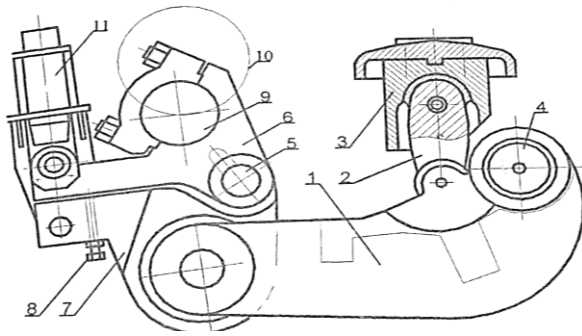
Конструкція механізму пресування коліно-важільного преса с розрізним шатуном: 1 – важіль пресового механізму; 2 – серга; 3 – поршень що пресує; 4 – вісь важеля, що жорстко зв'язана з рамою преса; 5 – вісь розрізного шатуна; 6 – верхня частина розрізного шатуна; 7 – нижня частина розрізного шатуна; 8 – болт, що регулює довжину шатуна; 9 – шийка колінчастого вала; 10 – траєкторія руху шийки колінчастого вала; 11 – гідро- чи пневмоциліндр
